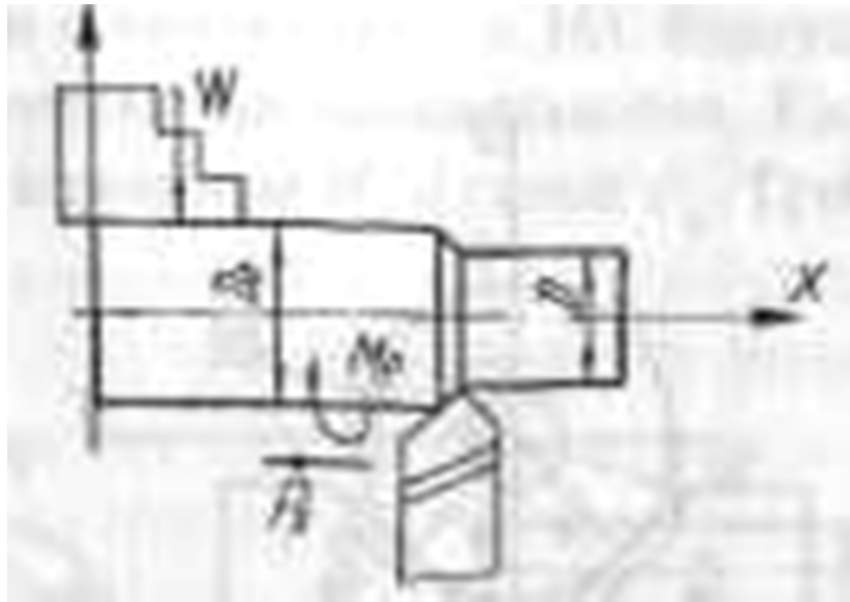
Схема для розрахунку сили закріплення заготовки
